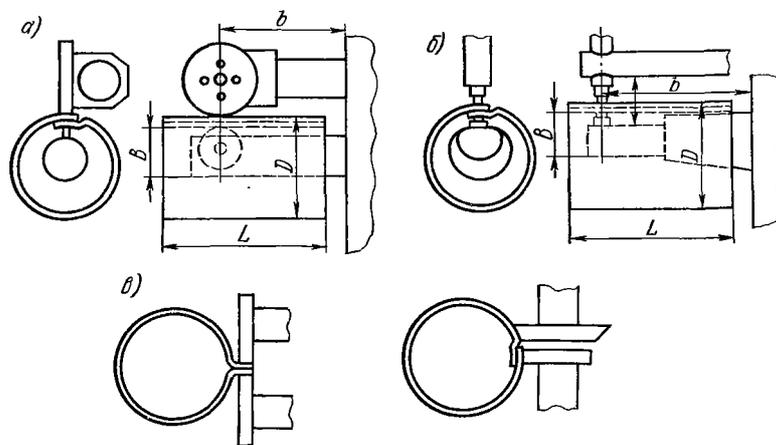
Схемы сварочных контуров шовной (а) и точечной (б) машин, а также схема создания точечных или шовных сварных соединений при изготовлении тонкостенных трубчатых элементов небольшой длины
